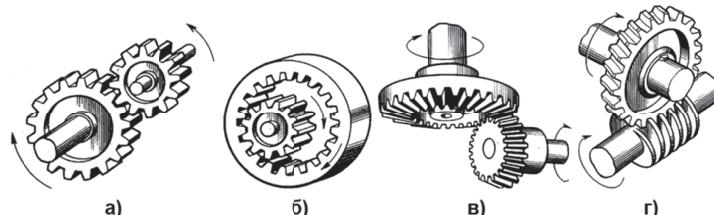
Зубчатые передачи (а – г) для вращательных движений
